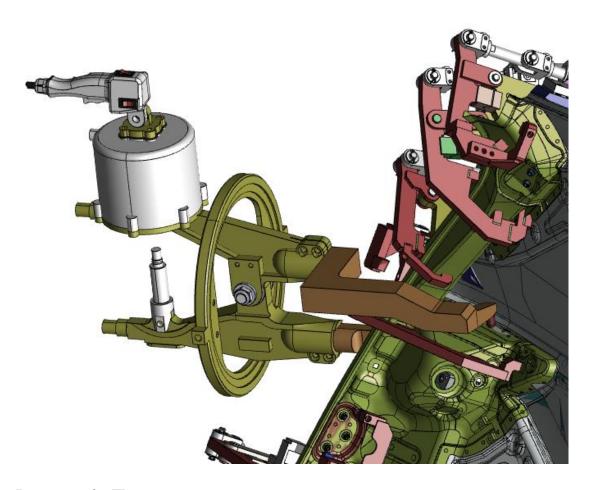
Положение сварочного пистолета при сварке зоны заднего фонаря
